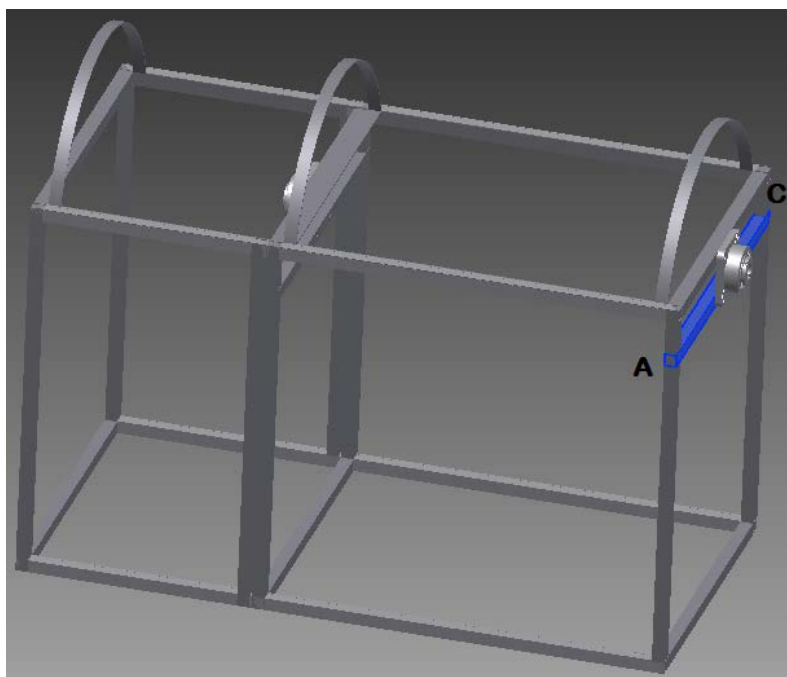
Estructura de la máquina, viga AC.¹⁰⁷
